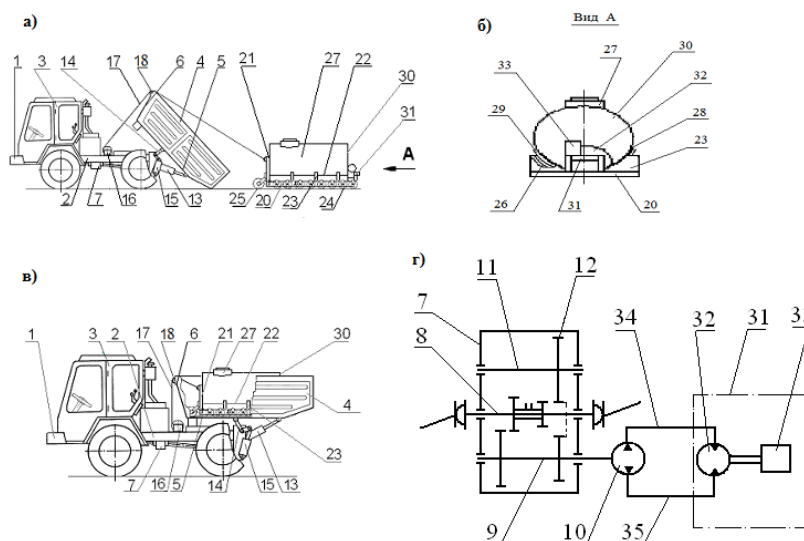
Поливальный агрегат на базе автотрактора: а – вид сбоку на агрегат при погрузке цистерны; б – вид А; в – вид сбоку на агрегат с цистерной в транспортном положении; г – гидрокинематическая схема привода водяной помпы
